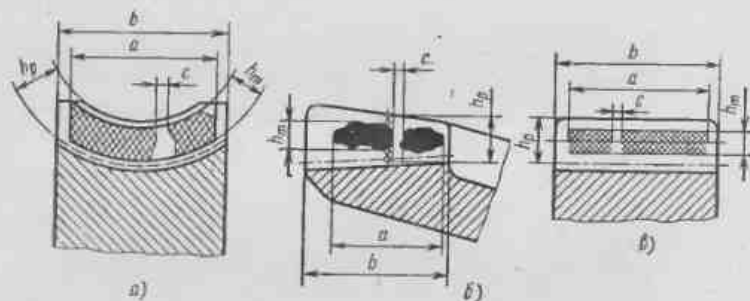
Пятно контакта зубьев в передаче: а — червячного колеса; б — цилиндрического зубчатого колеса; а — коническое зубчатое колеса
